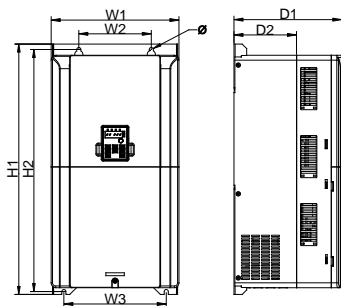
Настенный монтаж ПЧ 3ф 380 В (45-75 кВт)
